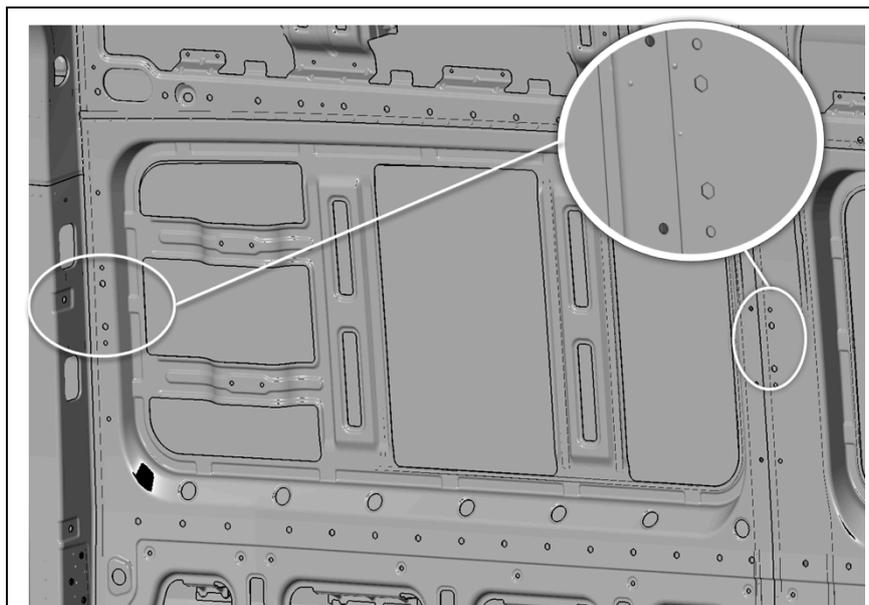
Preinstalación de estantería en la carrocería (pared lateral), ejemplo: carril Airliner instalado en la pared lateral
